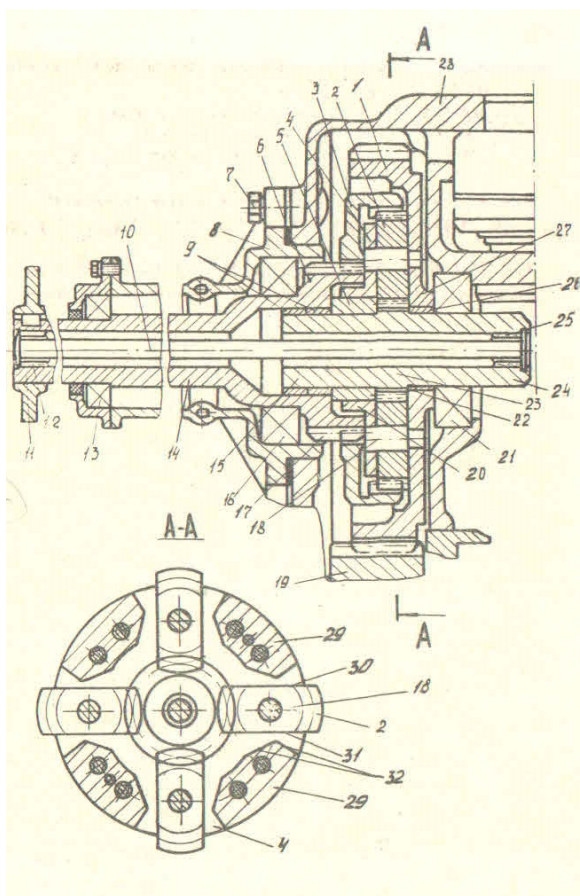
Упруго-эластичный привод конечной передачи транспортного средства
